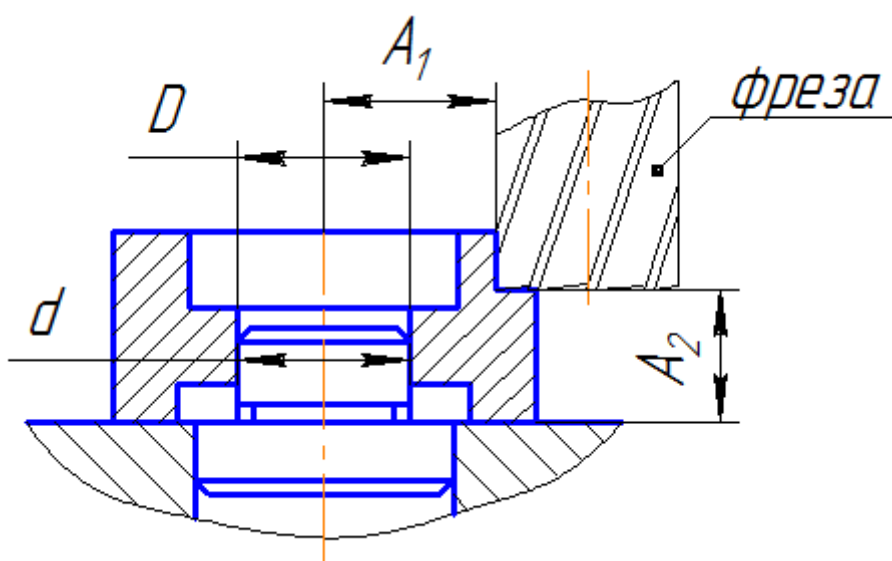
Установка ступенчатой втулки на жесткий цилиндрический палец
